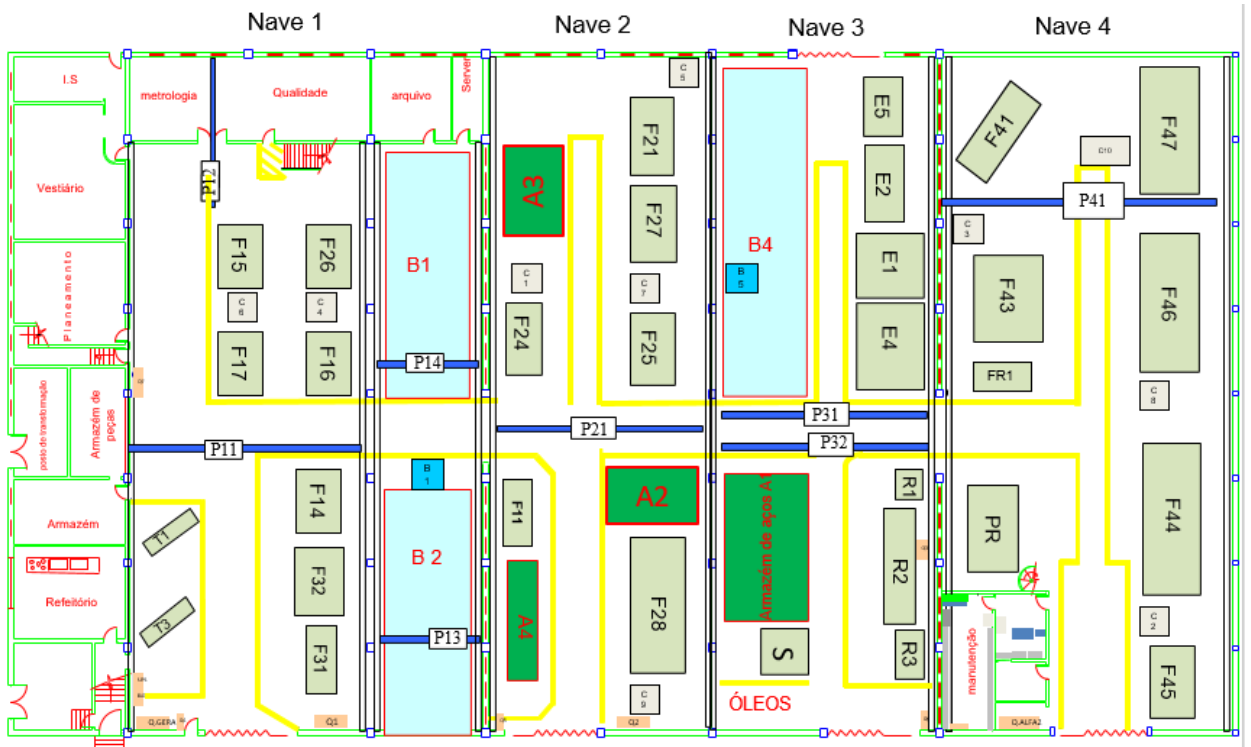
Proposta de novo Layout - Layout 1 -(escala 1:200)
